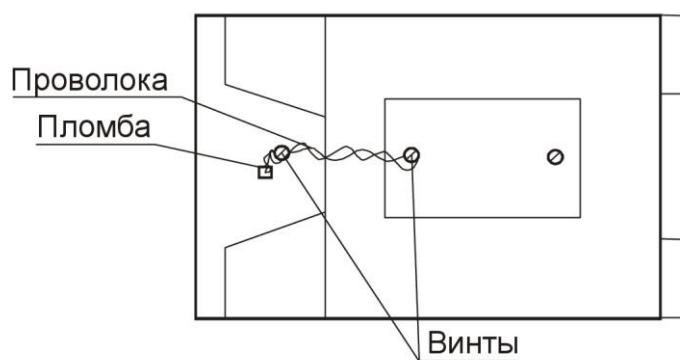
Схема пломбировки вторичного преобразователя при креплении на DIN-рейку
